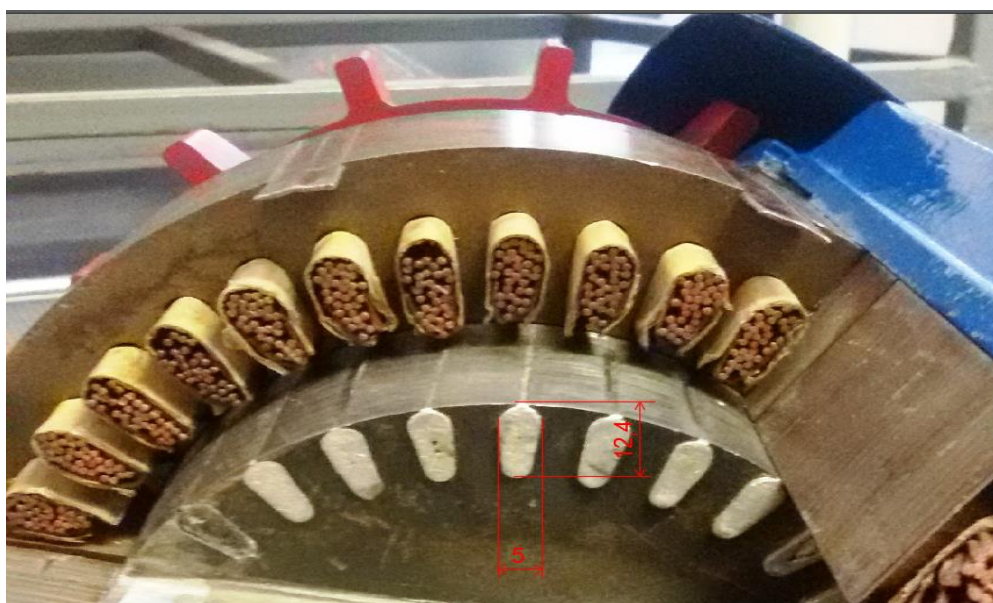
Stroj pro konstrukční měření a měřený motor
